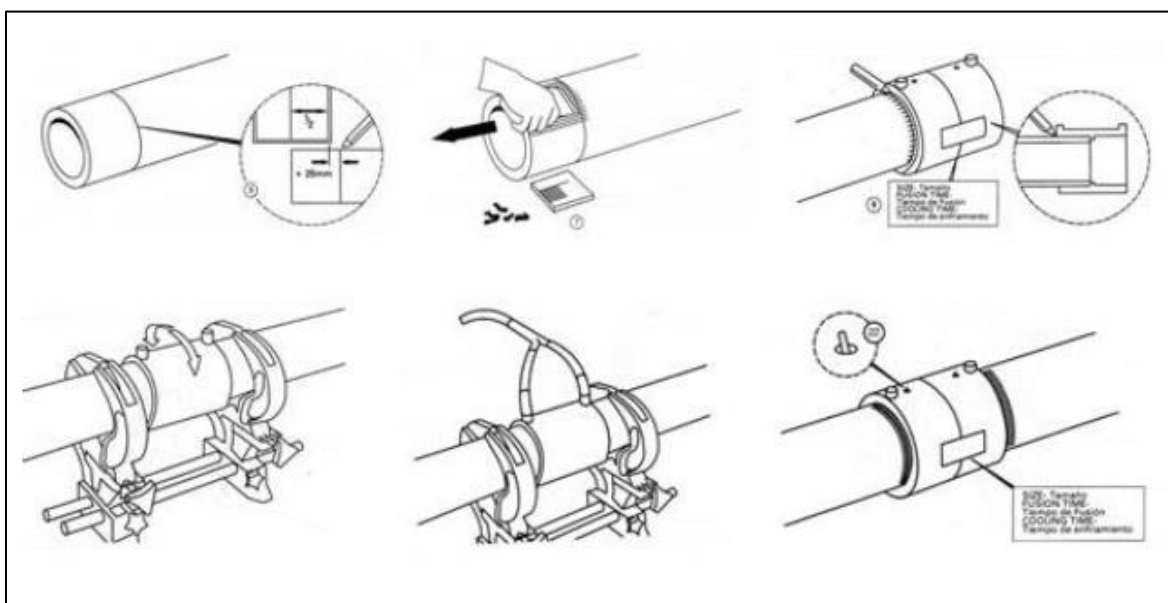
Passos a seguir per realitzar una soldadura per electrofusió.
